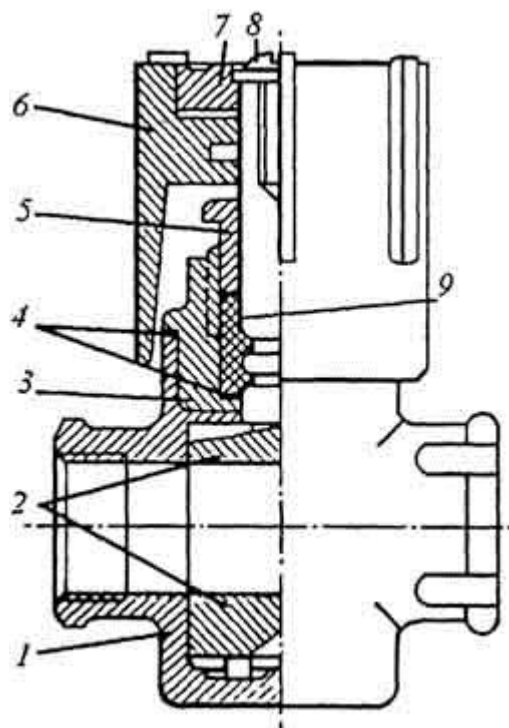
Кран регулирующий трехходовой типа КРТП: 1 - корпус; 2 - заслонка; 3 - крышка; 4 - прокладки; 5 - гайка сальника; 6 - рукоятка; 7- крышка-указатель; 8 - винт с шайбой; 9 - сальниковое уплотнение
